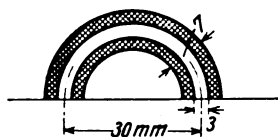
Abmessungen des Spannungsmessers, endgültige Ausführung.
